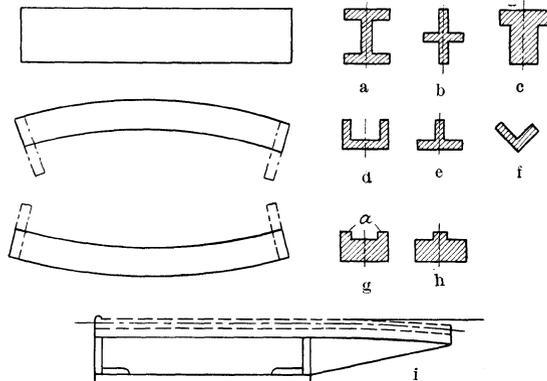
bis i. Querschnittsformen und Körpergestaltung mit Rücksicht auf Spannungen.
